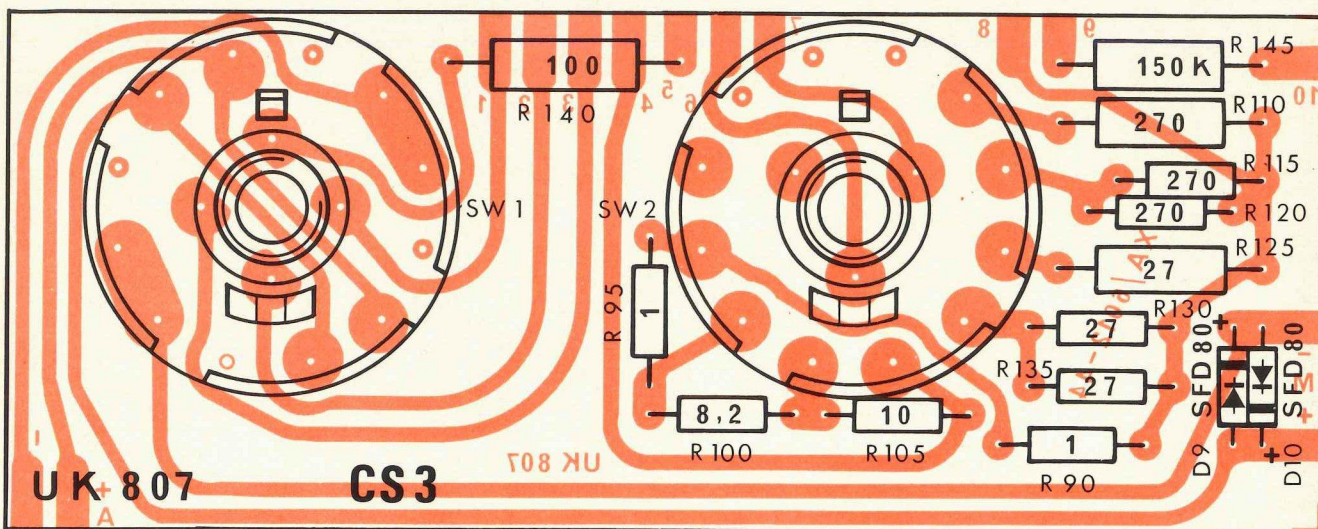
Montaggio dei componenti sul circuito stampato C.S. 3.
